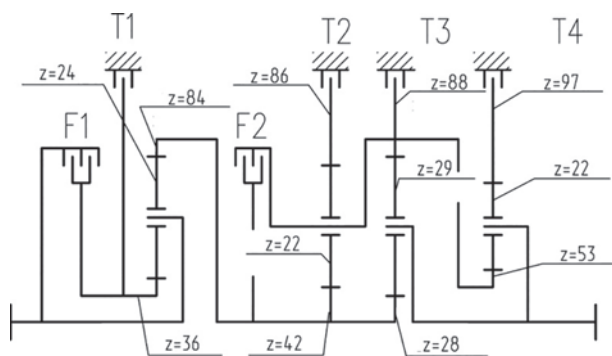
Кинематическая схема ПКП карьерного самосвала БЕЛАЗ-7555Н
